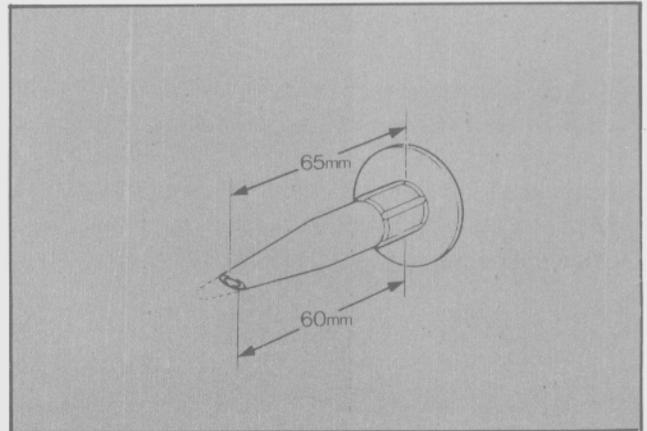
Primer corte a realizar en la boquilla aplicadora de adhesivo.
